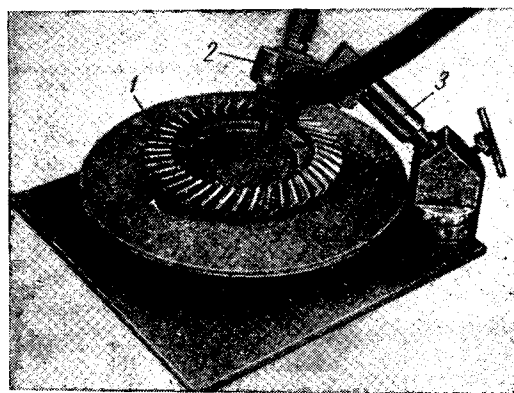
Внешний вид приспособления для гидроабразивной очистки ведомых шестерен 12-2402060:
